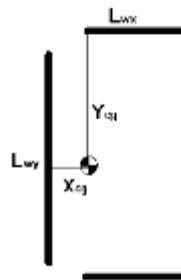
Clasificación de Soldadura. Fuente: Propia realizado en AUTCAD.
